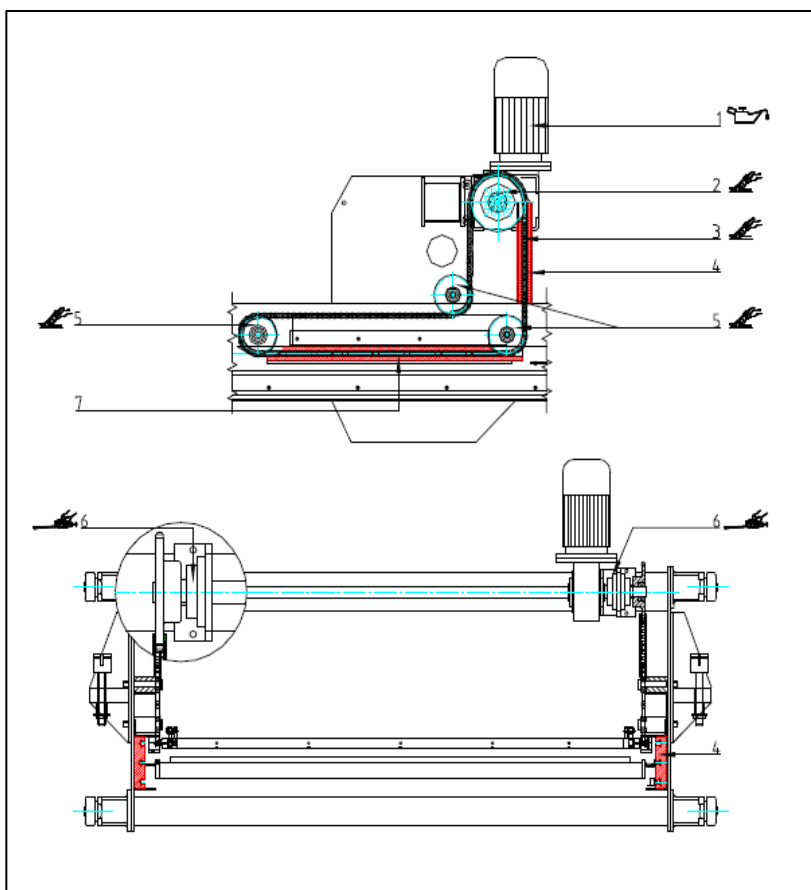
Imagen de Despiece del Equipo: Empujador Motorizado.
